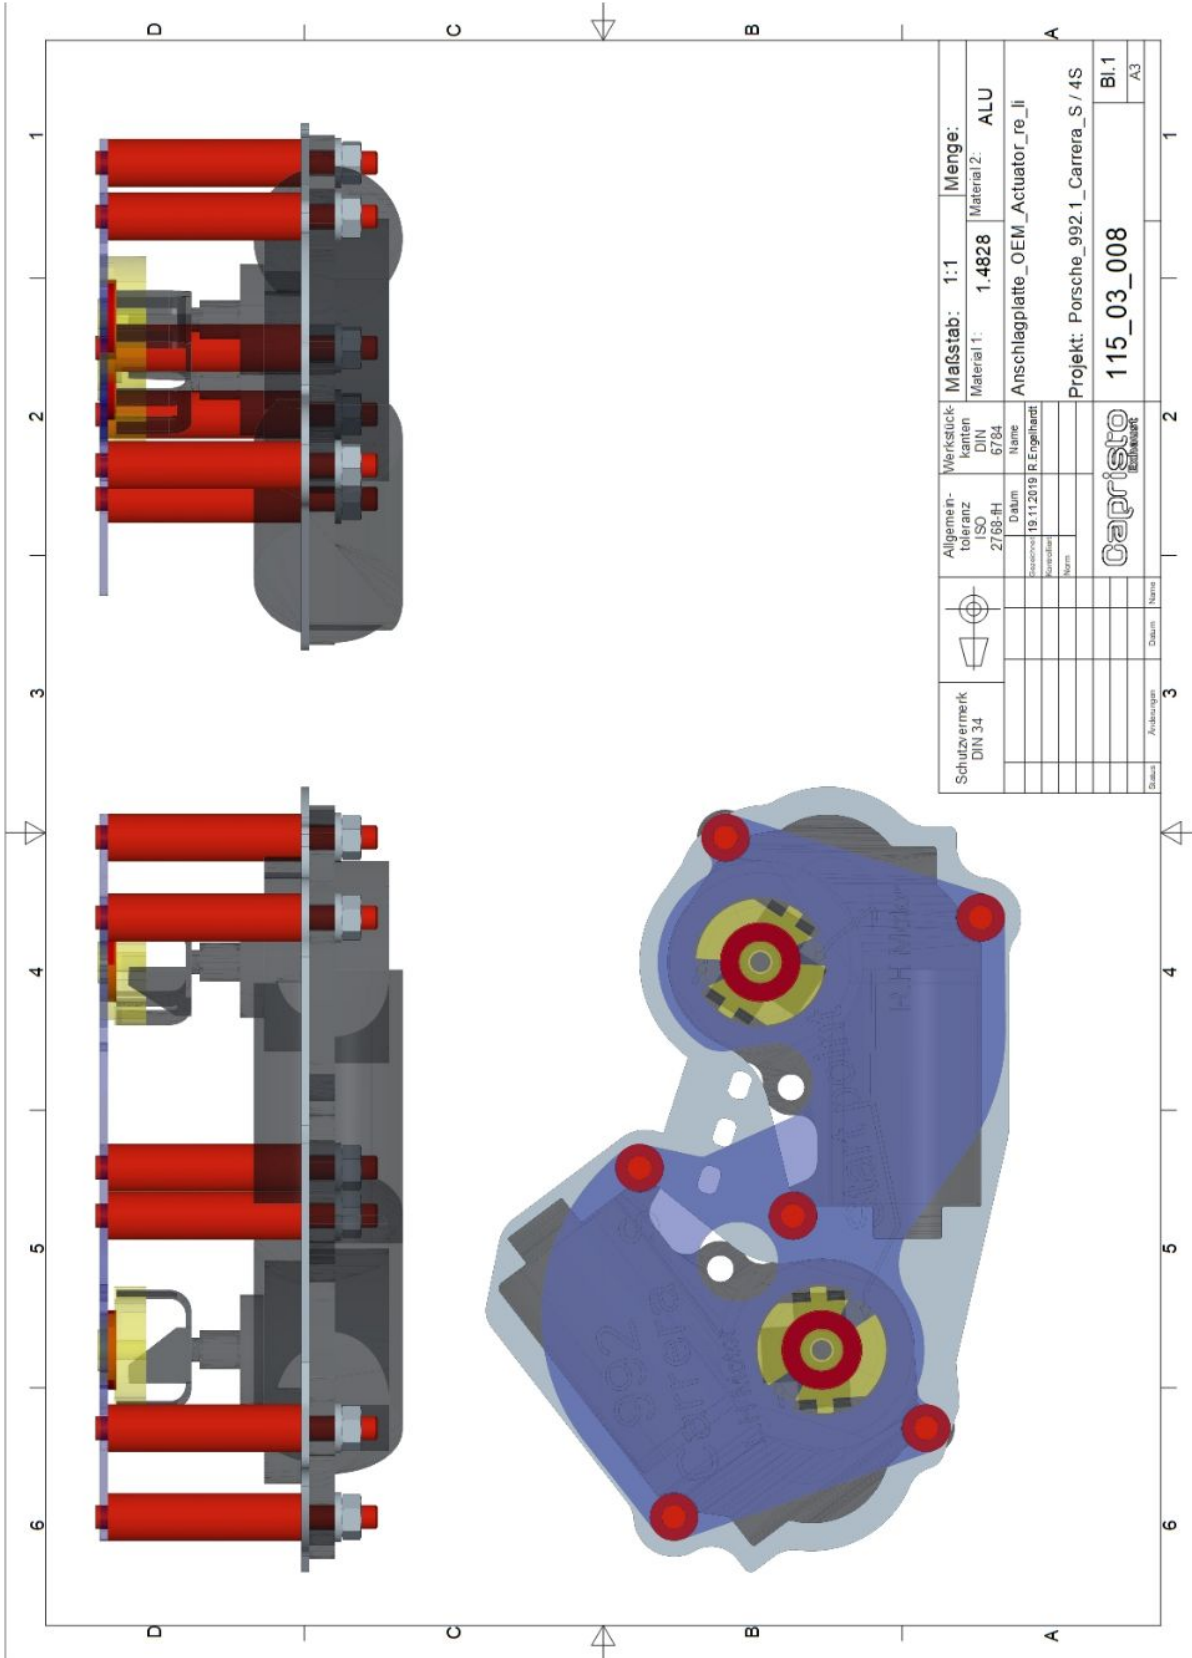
Zeichnung Anschlagplatte OEM Actuator
